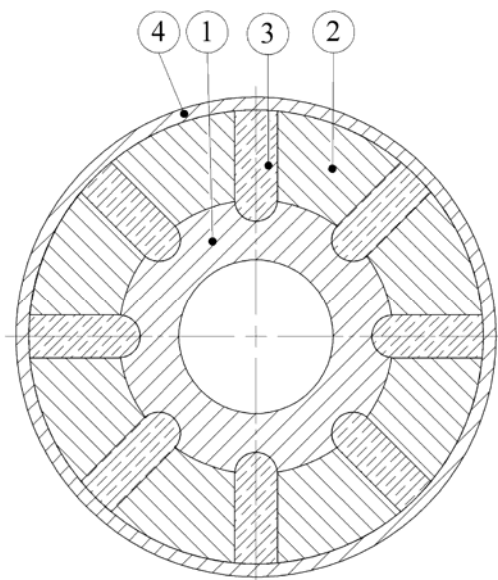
Конструктивная схема ротора с тангенциальным намагничиванием; 1- немагнитный вал; 2-полюс; 3-магнит; 4- немагнитный бандаж.
